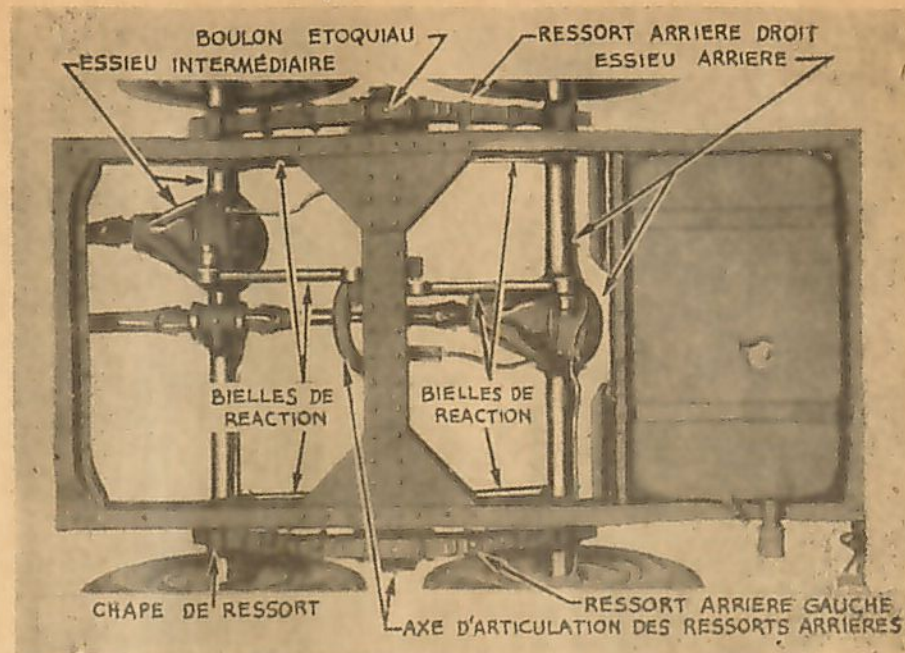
Vue de la suspension arrière sur châssis 1 1/2 T. 6 × 6.
